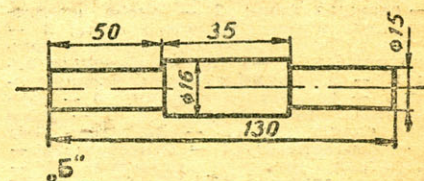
Вал, установленный вместо вала сцепления двигателя Д-4 с муфтой (Б — на рис. 5).
